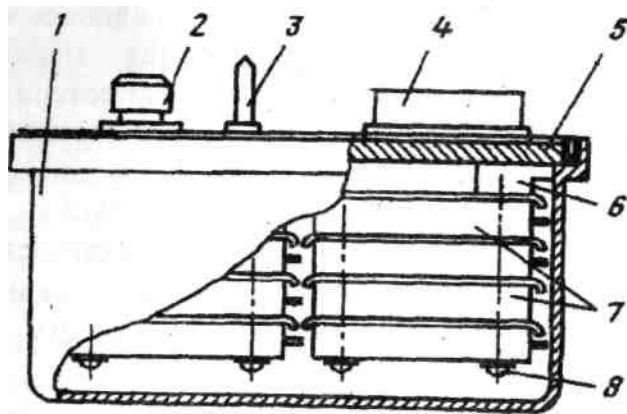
Этажерочная конструкция блока приемопередающего устройства 4-го поколения: 1 – кожух; 2 – высокочастотный разъем с полиэтиленовой заглушкой;
